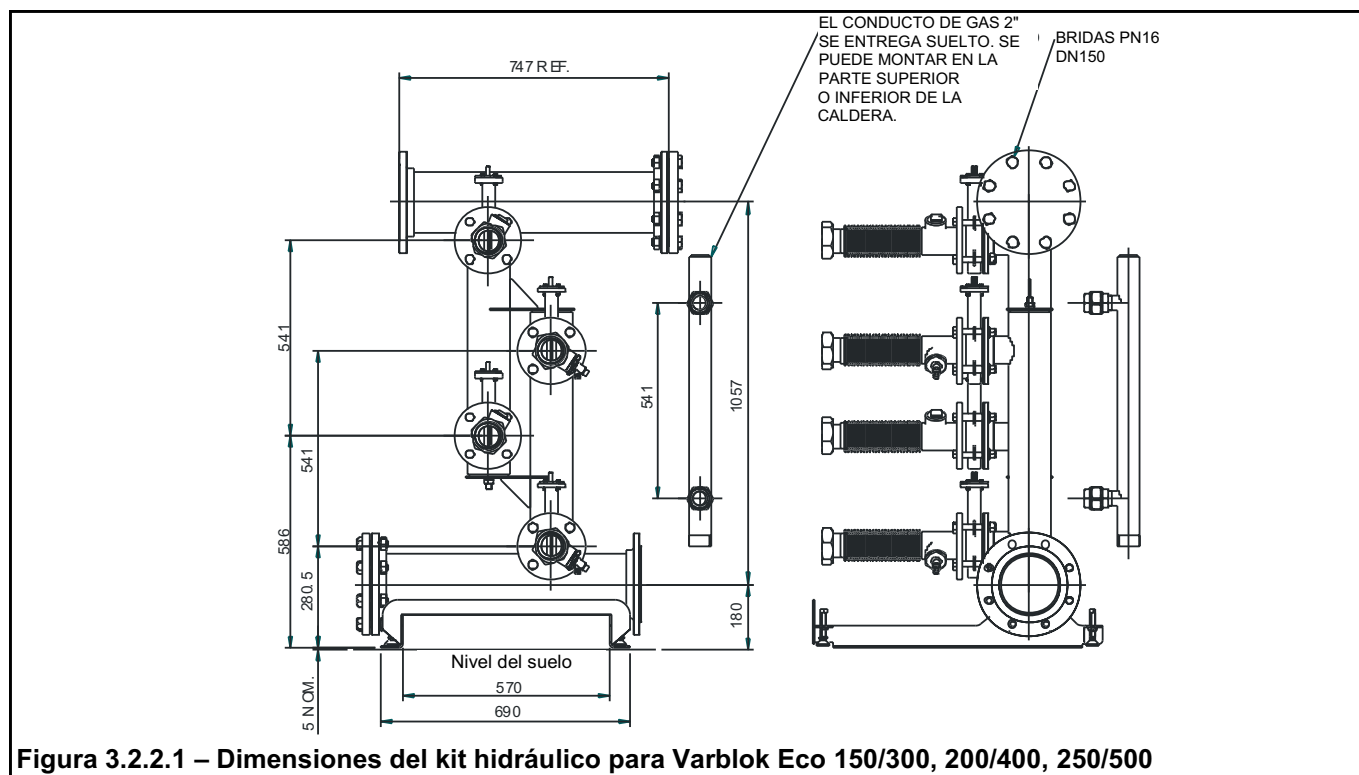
Dimensiones del kit hidráulico para Varblok Eco 150/300, 200/400, 250/500
